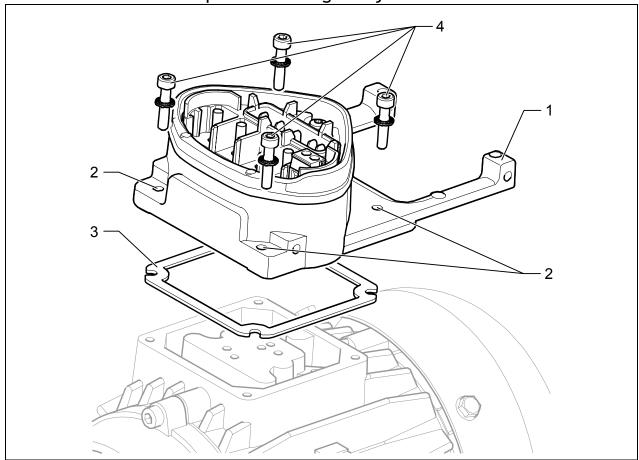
Ordre d'assemblage: boîtier de raccordement - plaque d'adaptation
